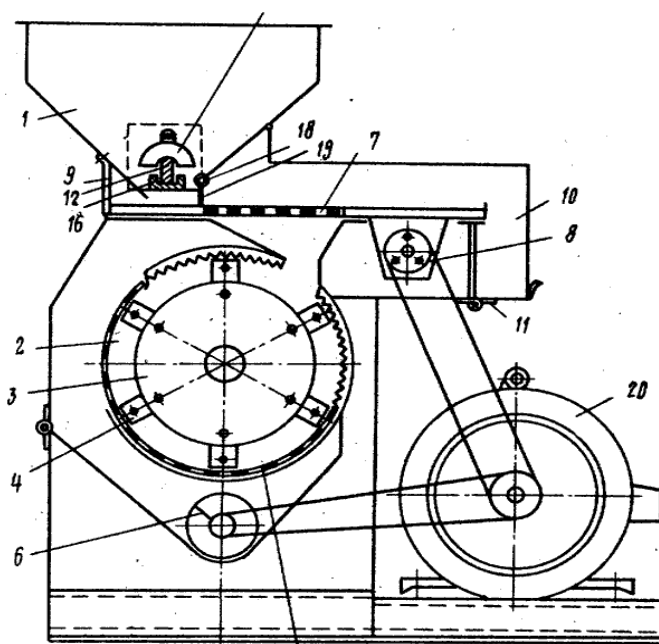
Дробака: 1 – бункер; 2 – електромагнітний сепаратор; 3 – вібралоток; 4 – робоча камери; 5 – сито; 6 – шнек; 7 – привод
